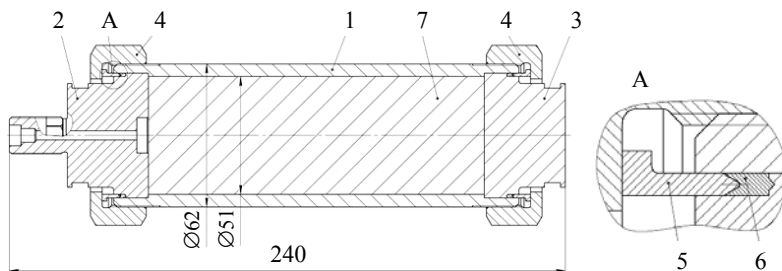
Конструкция прочностного макета из алюминиевого сплава 6061: 1 – обечайка; 2, 3 – крышка; 4 – гайка; 5 – кольцо; 6 – прокладка; 7 – вкладыш
